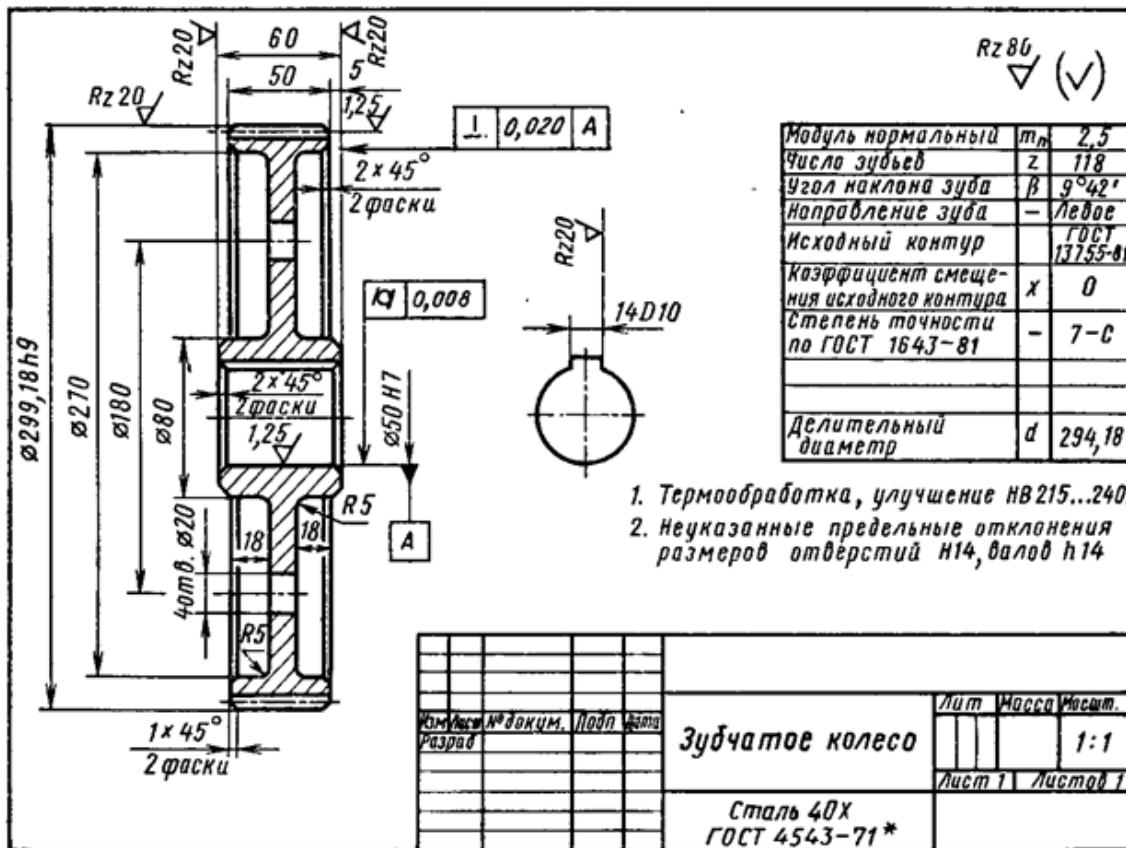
Чертёж цилиндрического зубчатого колеса редуктора
